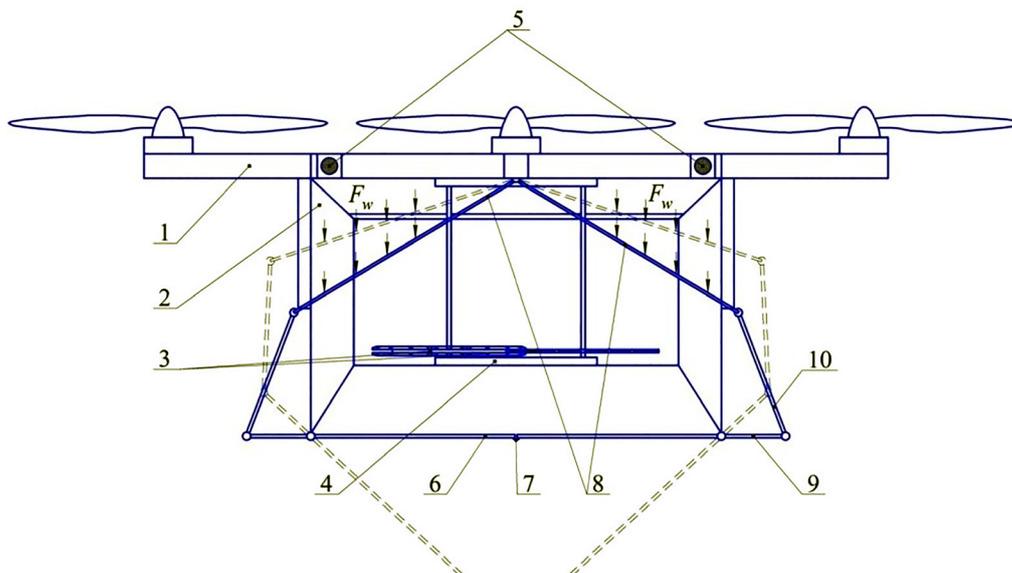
Общий вид БПЛА для уборки зерновых культур
